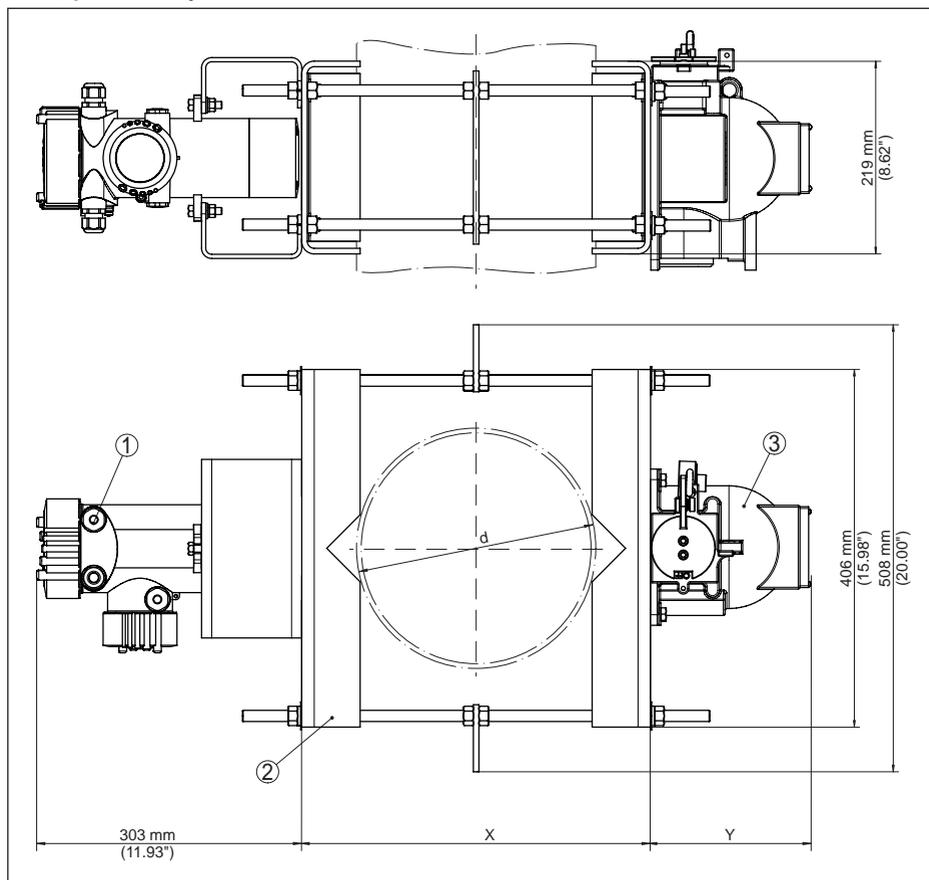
Dispositivo de sujeción con contenedor de protección de fuente radiactiva SHLD1 y sensor montado horizontalmente
